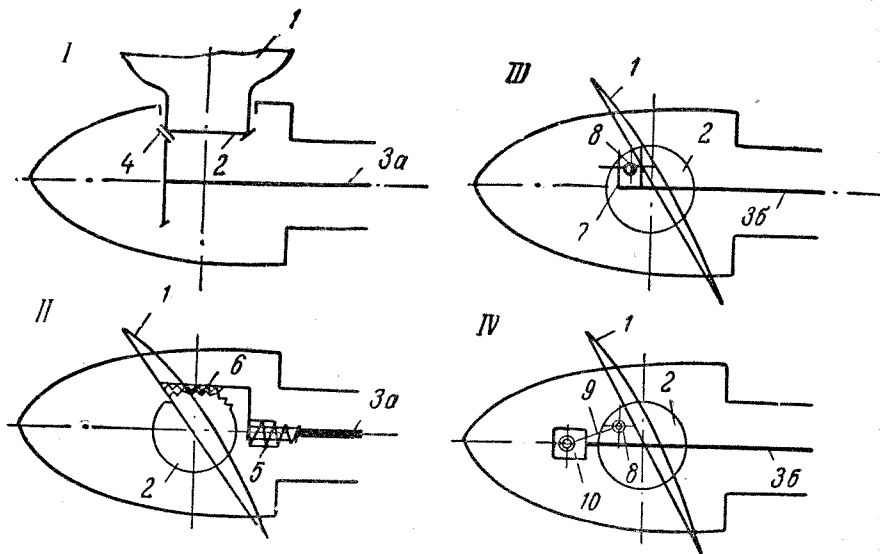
Схемы механизмов поворота лопастей ВРШ: I — шестеренчатый; II — винтовой; III — поводковый; IV — шатунный
